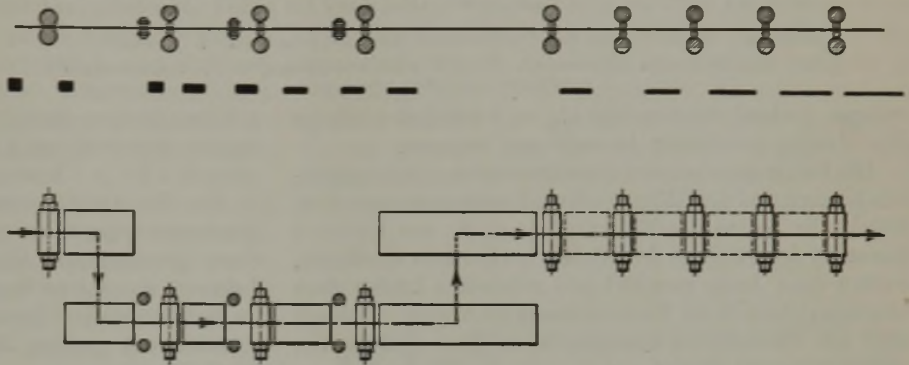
Kontinuierliches Warmwalzwerk der Weirton Steel Co.
